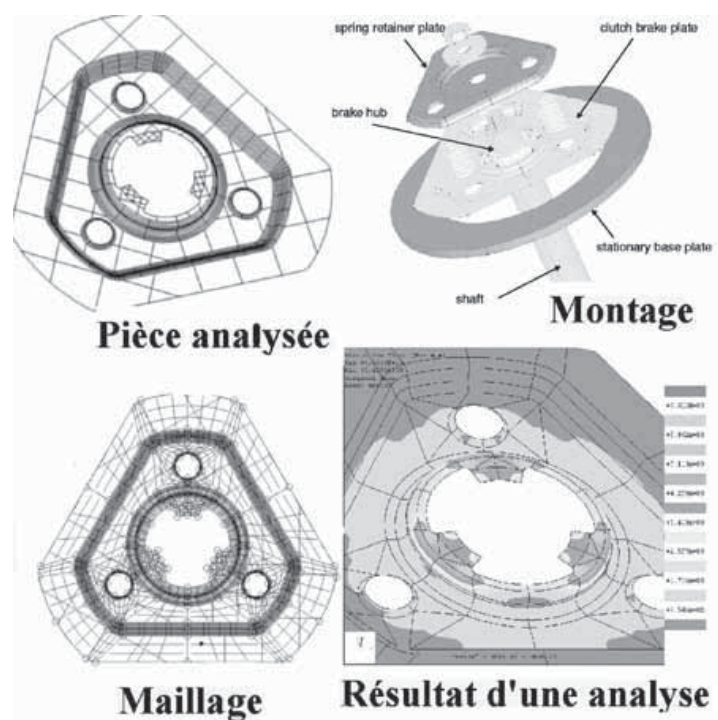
Planches générées avec Pro/ENGINEER et le module Structure de Pro/MECHANICA
